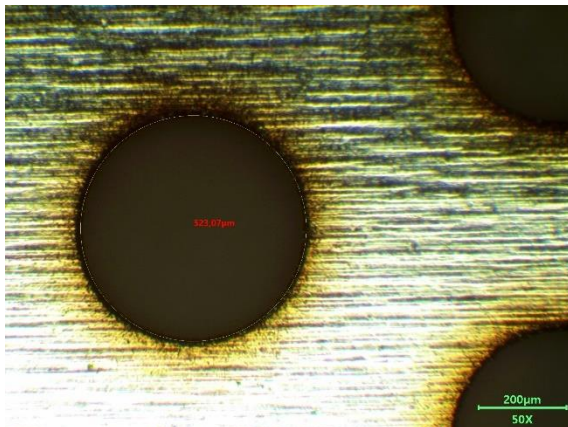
Detailansicht einer LASER-Bohrung für den Assembly-Rahmen; Durchmesser etwa 50µm
